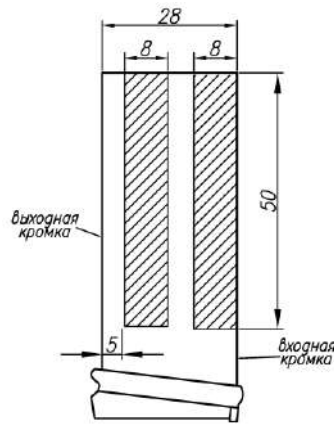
Схема вирізки зразків із пера лопатки
